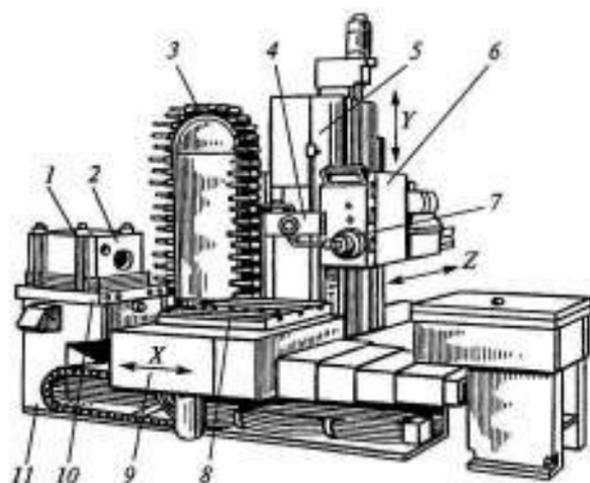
Многоцелевой сверлильно-фрезерно-расточный станок для обработки корпусных деталей:
